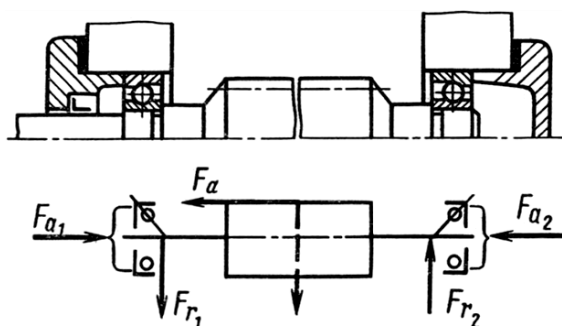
Подшипниковые узлы вала червяка и схема его нагружения
